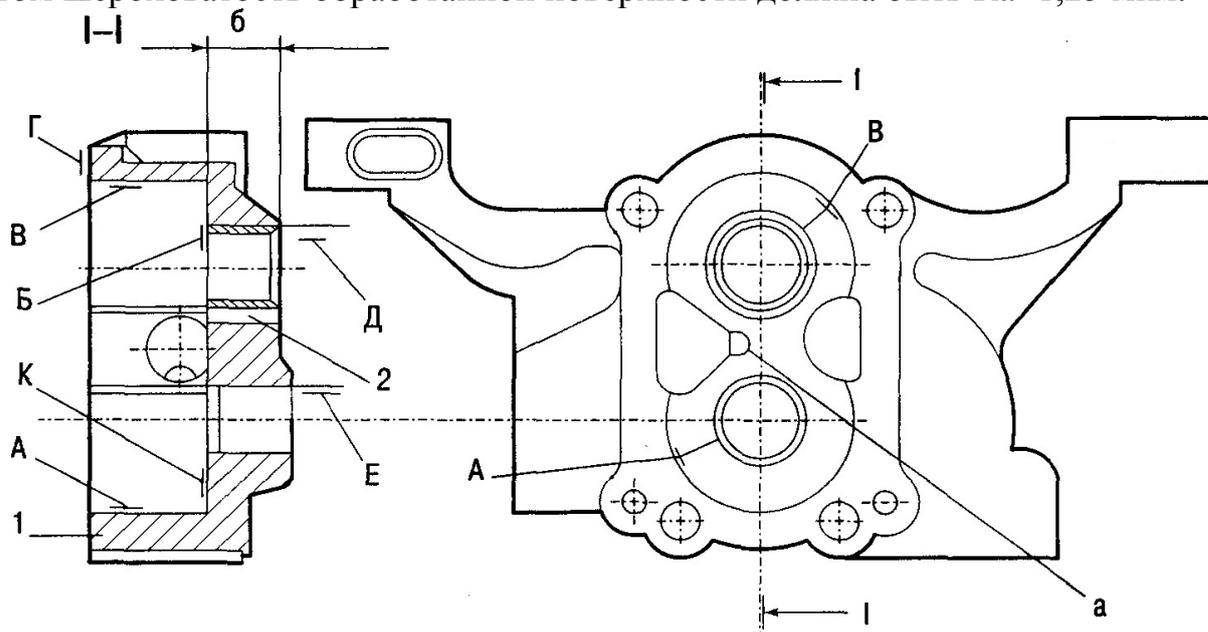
Корпус масляного насоса в сборе со втулкой: 1 - корпус; 2 - втулка; А, Б, В, Г, Д, Е, К - поверхности; а и б - размеры
